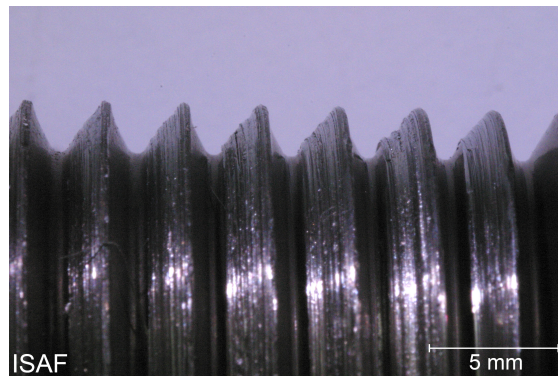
Gewindeprüfkörper axial belastet mit 220kN (Bolzen)
